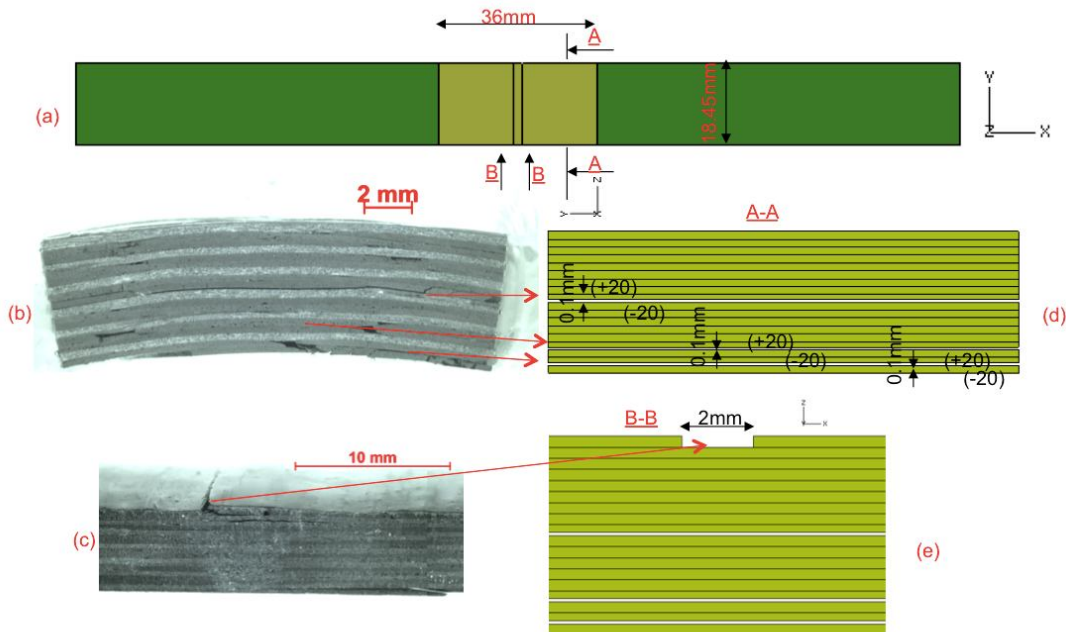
Dimension des défauts initiaux (a), endommagement généré par choc à 19J sur une coupe de l'éprouvette de la structure 3 (b), sur le bord d'éprouvette (c), dimensions des endommagements modélisés sur la coupe à 90° (A-A) (d), sur le bord d'éprouvette (e)
